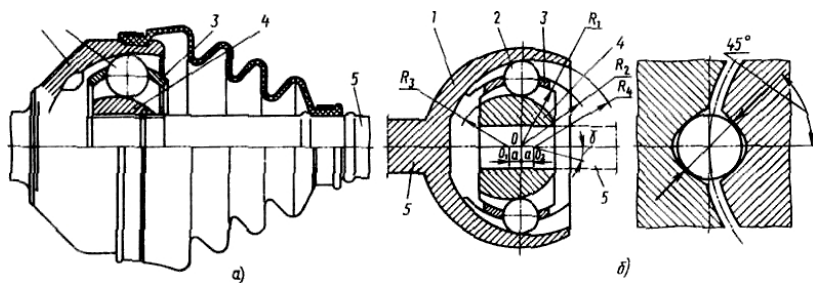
Карданный шарнир типа «Бирфильд»: *a* — конструкция; *б* — схема; 1 — корпус; 2 — шарики; 3 — сепаратор; 4 — кулак; 5 — вал
